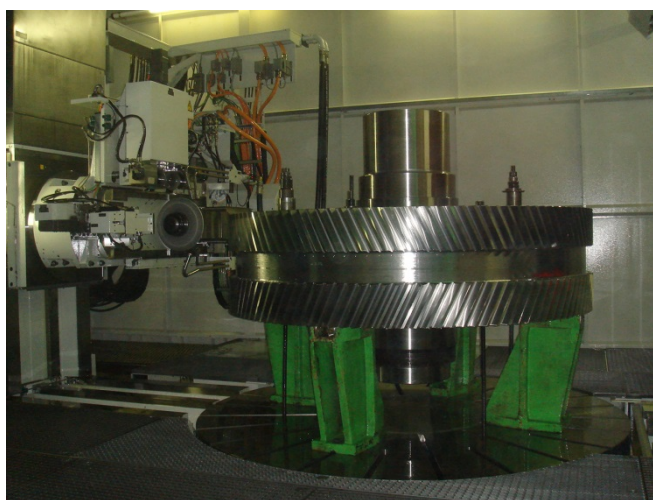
Обработка шевронного колеса червячной твердосплавной фрезой
